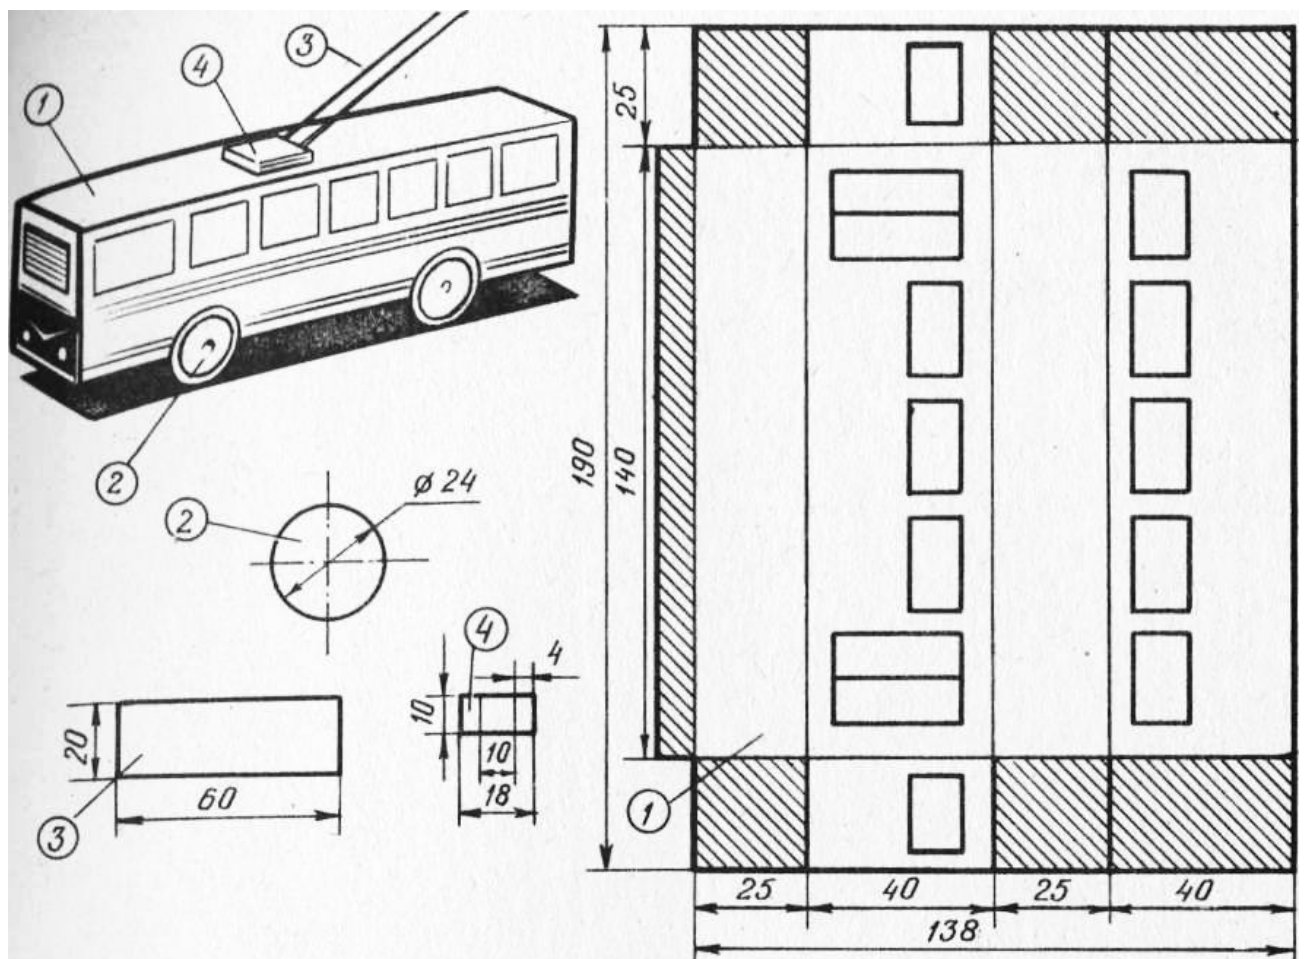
Модель троллейбуса: 1 — развертка кузова; 2 — колесо; 3 — заготовка для штанги; 4 — кронштейн
